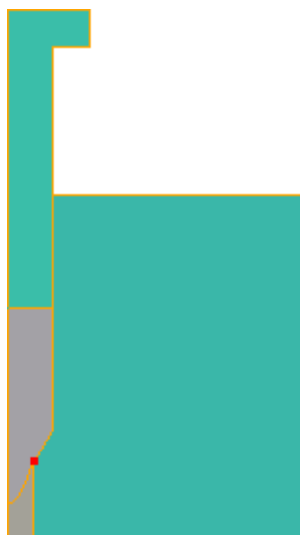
Формоутворення біметалевої заготовки,
